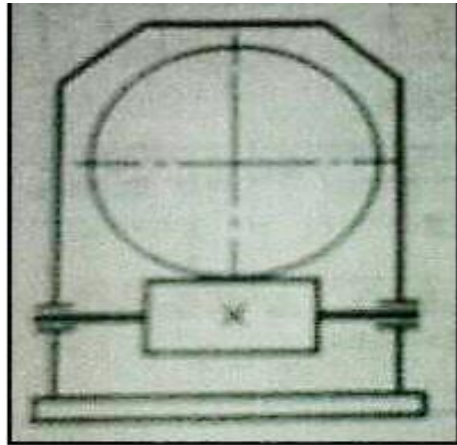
Кінематична схема одноступінчастого черв'ячного редуктора
